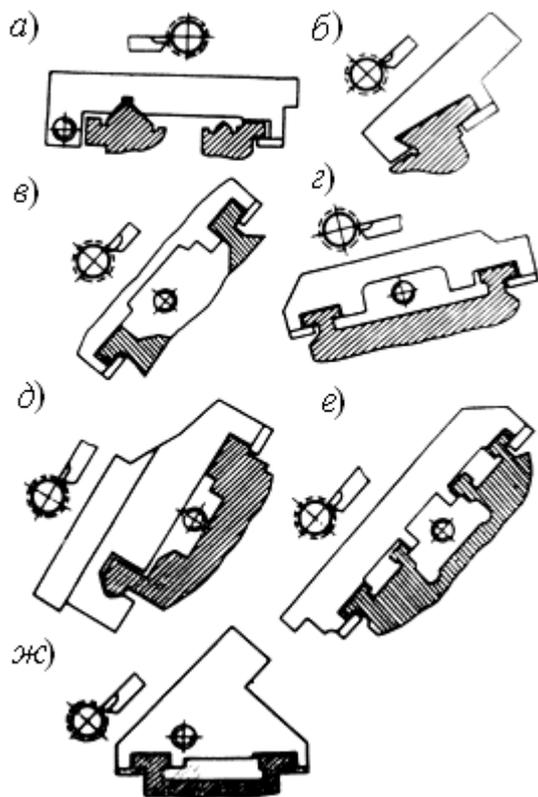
Направляющие скольжения суппортов односуппортных токарных станков
